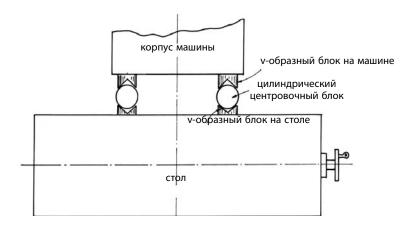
Выставка по центру на фрезерном станке (вид сверху)
